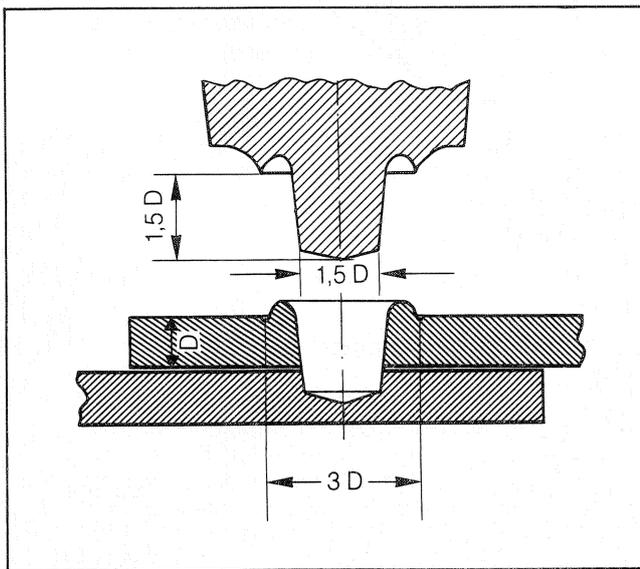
Prinzip des Ultraschall-Punktschweißens
